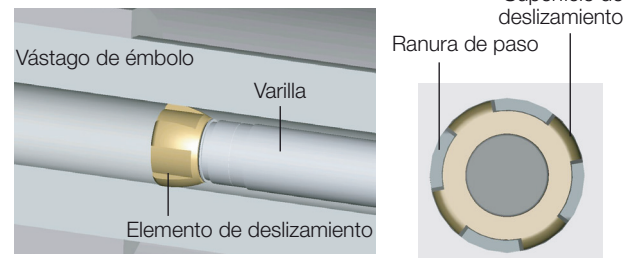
Vista detallada y vista desde arriba del elemento de deslizamiento
